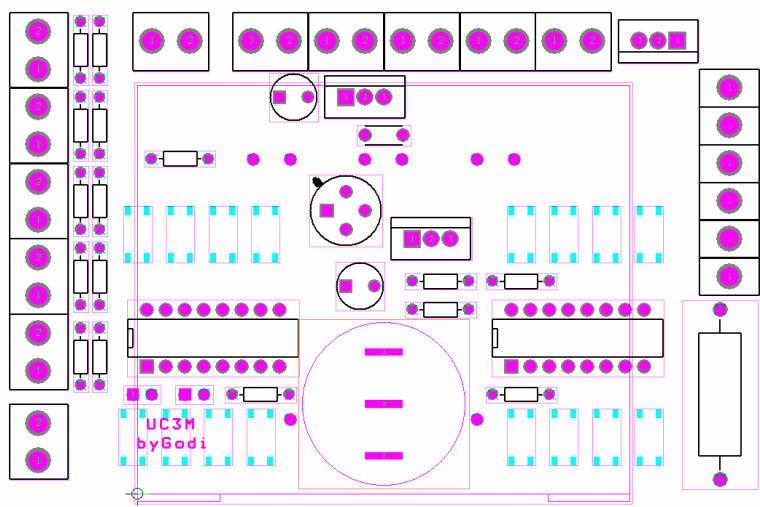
Emplazamiento de los componentes en la PCB diseñada.
